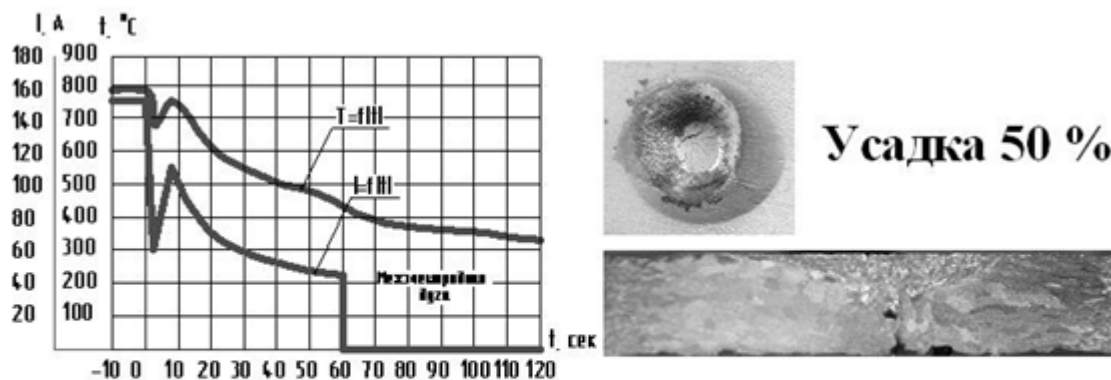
Термический цикл, форма и размеры усадочного кратера при реализации комбинированной кривой спада тока сварки
